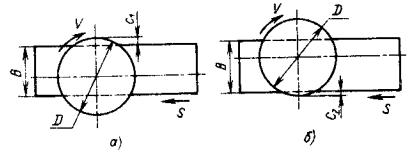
Расположение стальной заготовки при торцовом фрезеровании относительно фрезы: а — врезание зуба фрезы при  $c_1 = (0,03 \div 0,05)D$ ; б — выход зуба фрезы при  $c_2 = 0$
